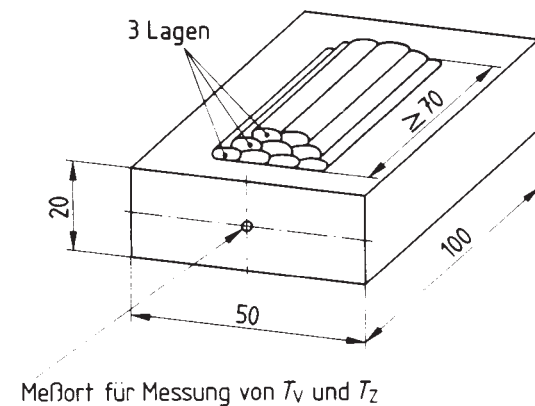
Prüfstück für das Lichtbogenschweißen (4-A2)
